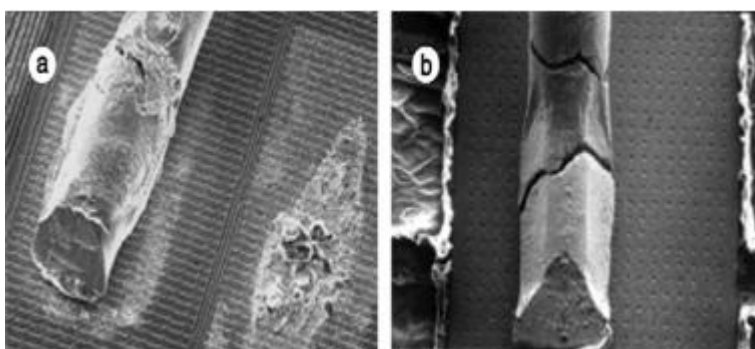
Observation au MEB de la levée d'un fil de bonding (a) et d'une fissure au niveau du pied du fil (b) [Cia02]
